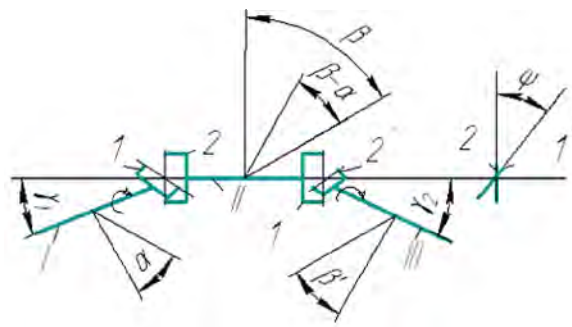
Схема карданной передачи с двумя шарнирами и обозначением углов
